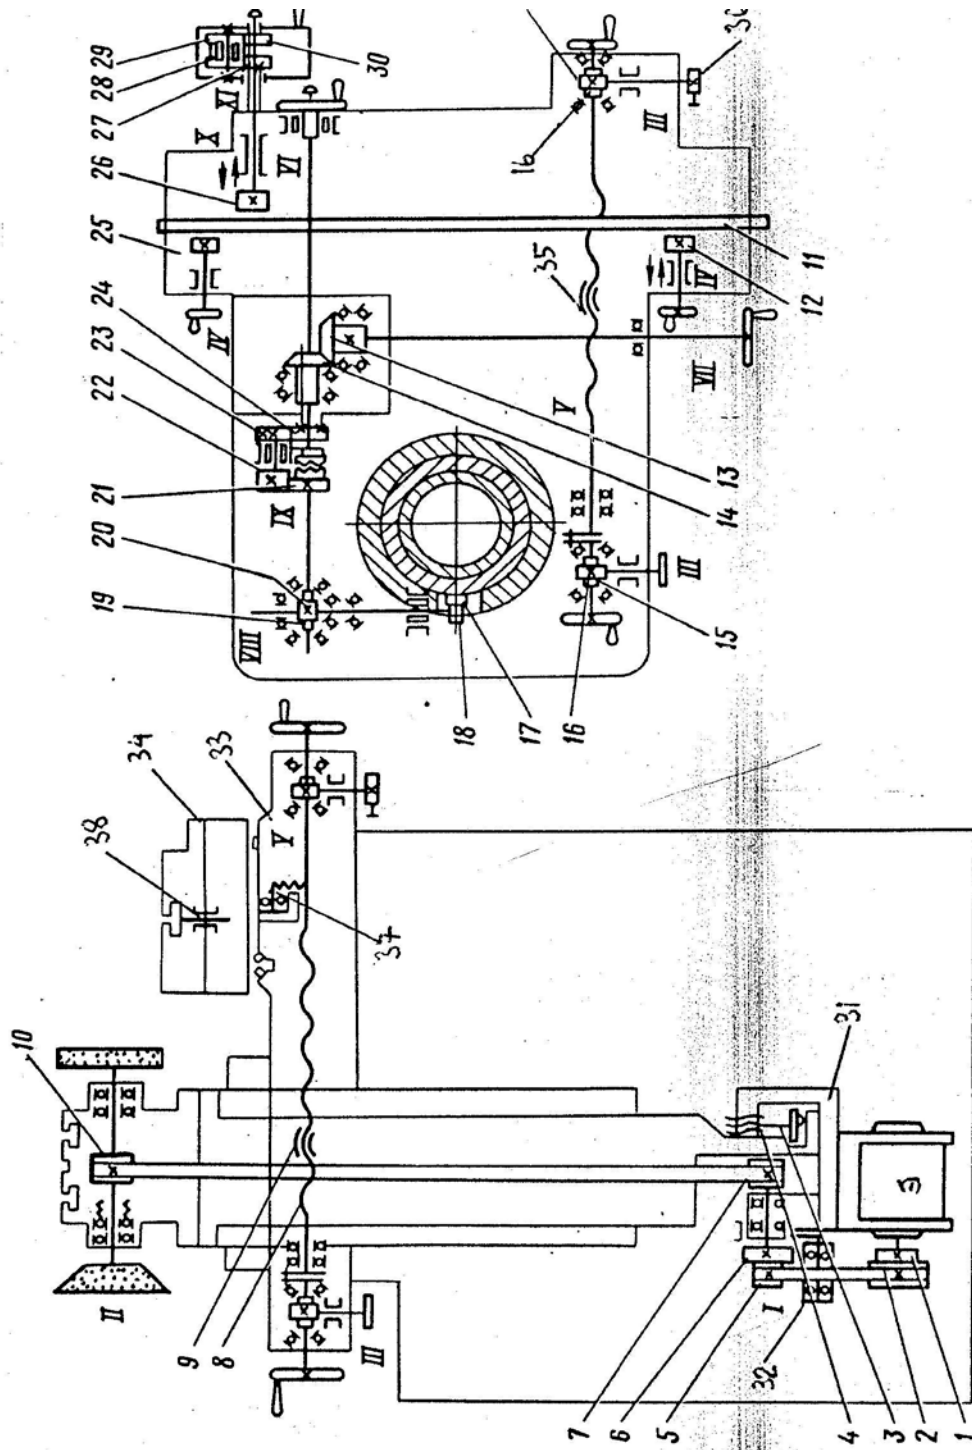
Кинематическая схема универсально-заточного станка 3B642
